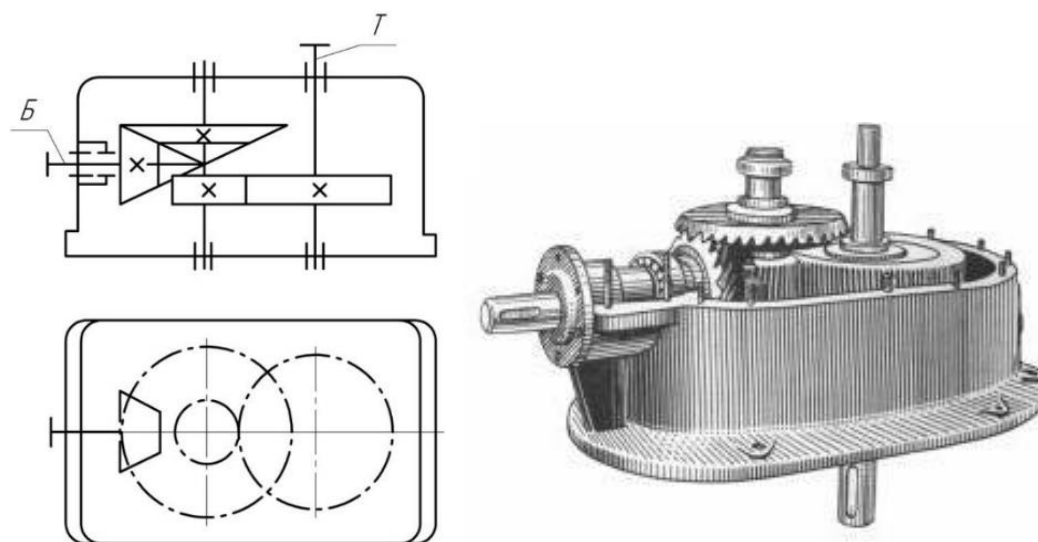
Двухступенчатый коническо-цилиндрический
